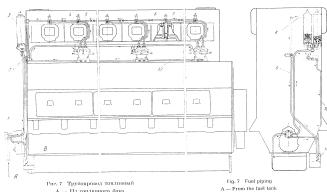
Трубопровод топлинный А — Из топливного бака В — Бачок слива топлина
